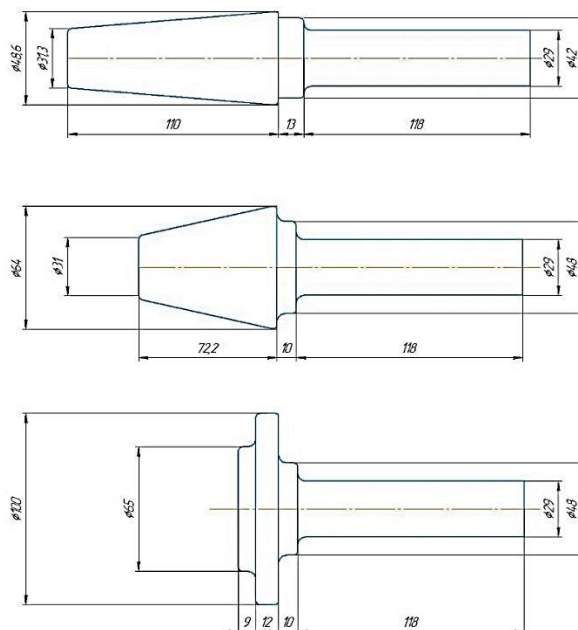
Переходы штамповки поковки детали «Вал».
